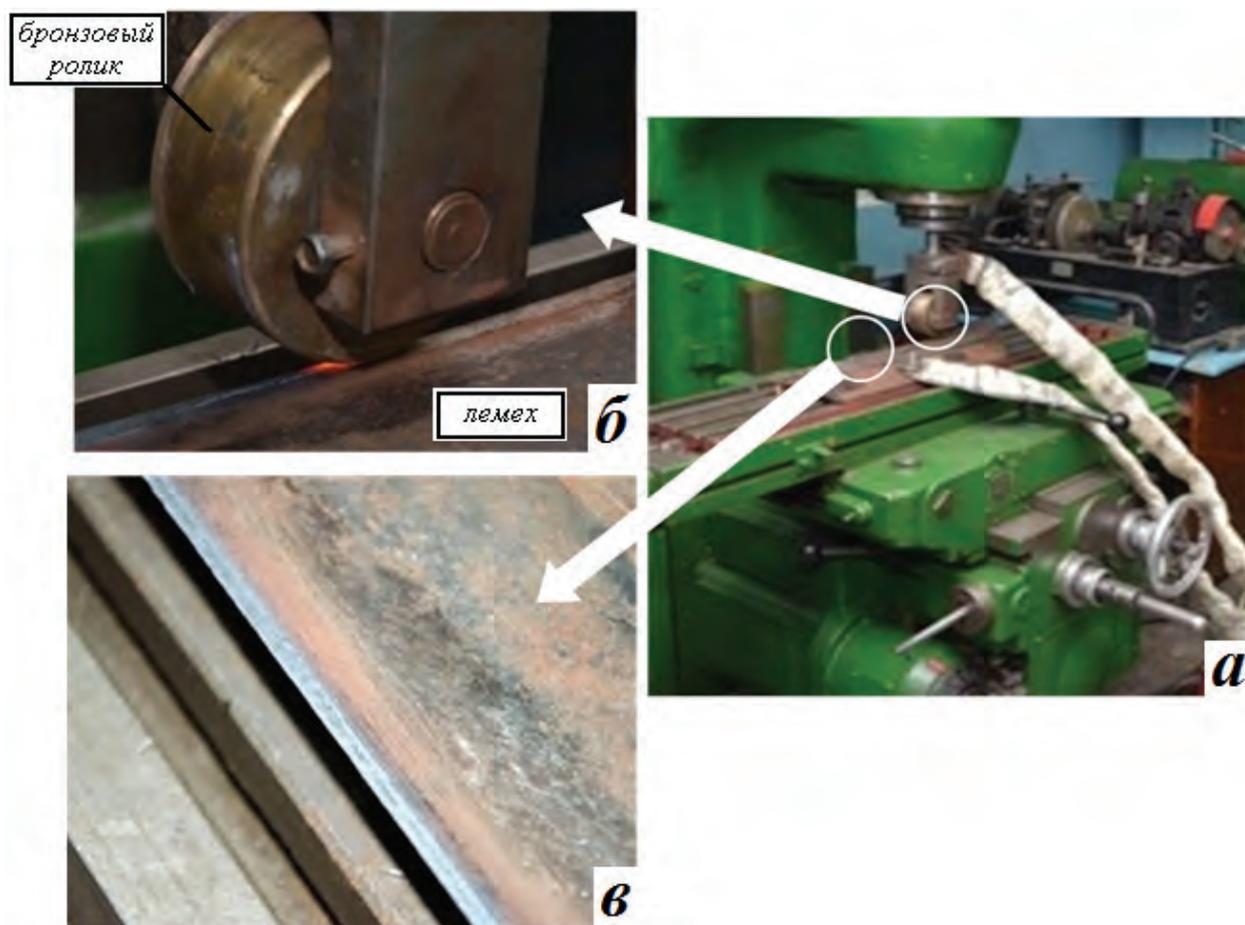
ЭМЗ рабочей поверхности лемеха: а – общий вид установки для ЭМЗ; б – процесс ЭМЗ; в - рабочая поверхность лемеха после ЭМЗ
